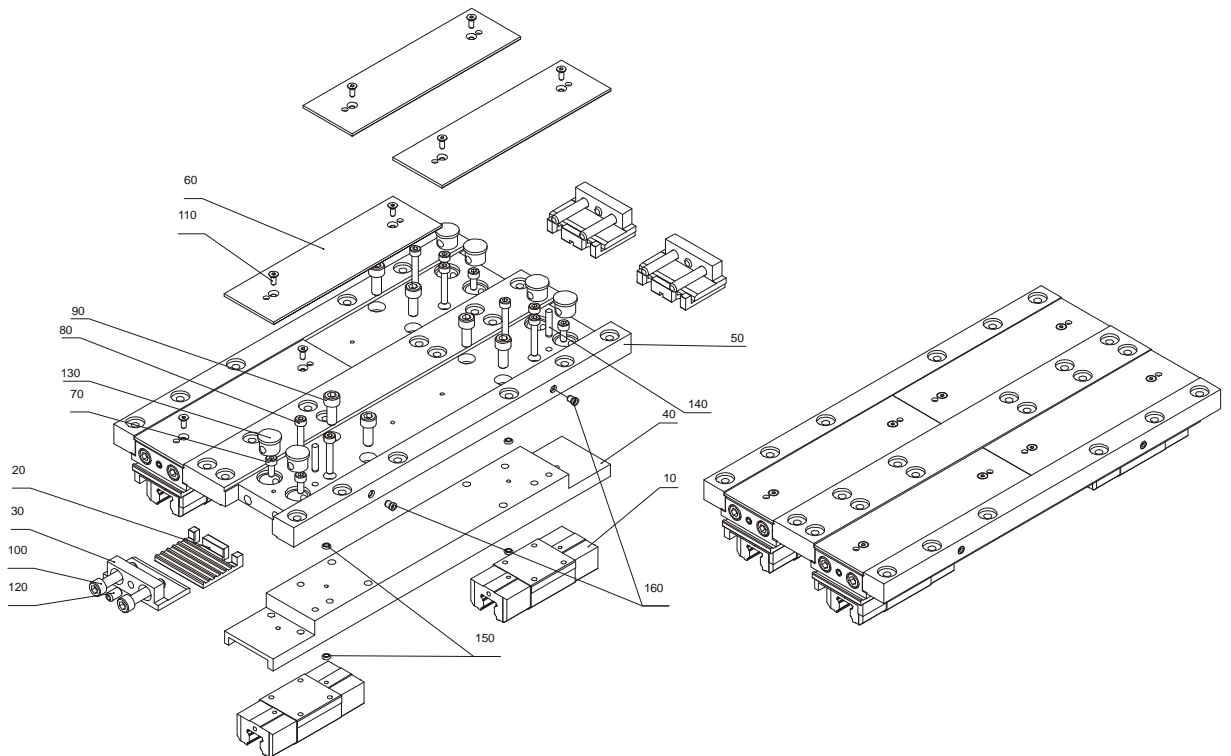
Modul 160/15, Langschlitten komplett, Explosionszeichnung
